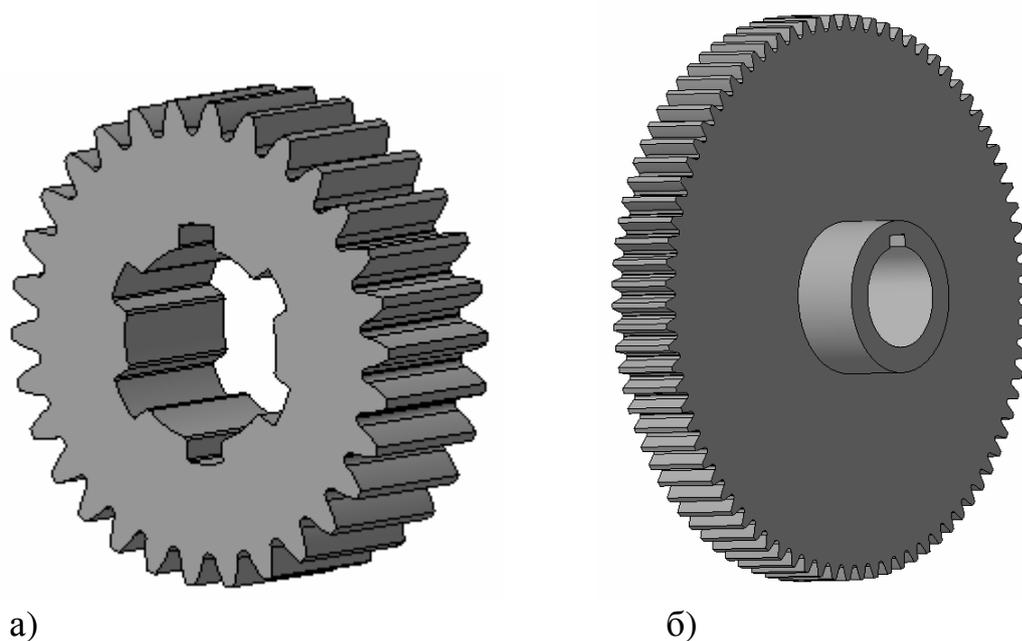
Твёрдотельные модели цилиндрических зубчатых колес
